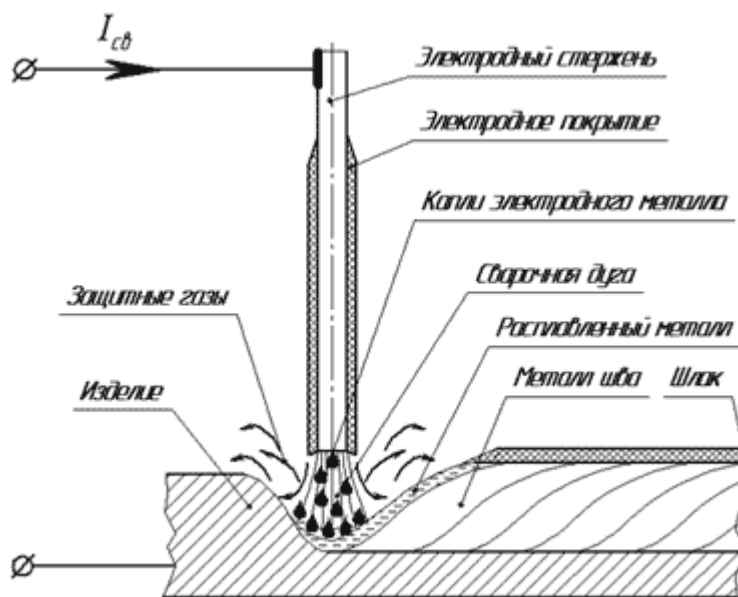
Схема сварки покрытым металлическим электродом
